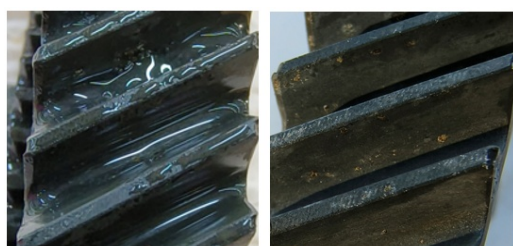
锈蚀缺陷齿轮及完好齿轮
